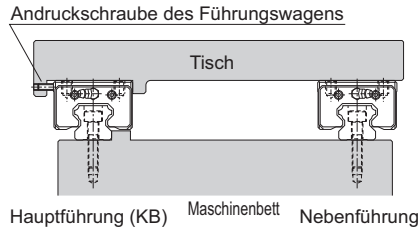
Beispiel für Montage ohne Andruckschrauben für Führungsschienen auf der Hauptführungsseite
